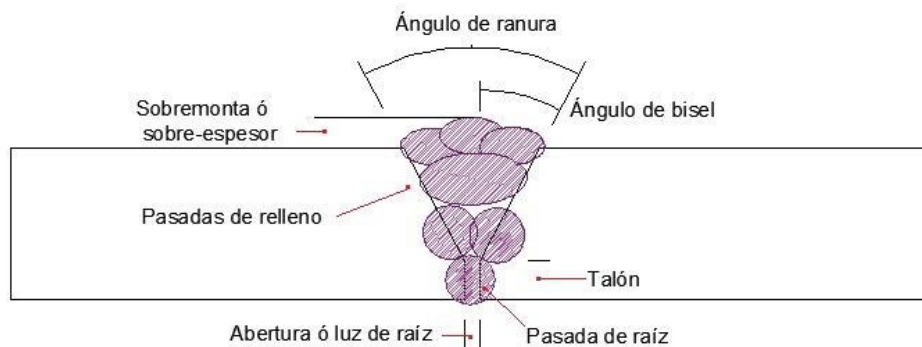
Parte de la unión soldada a tope en V.
